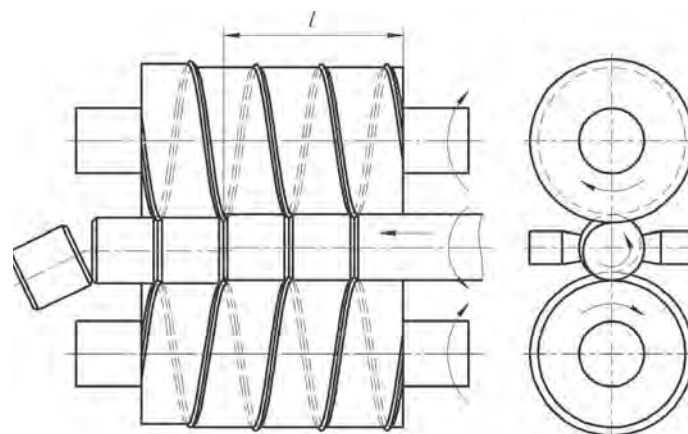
Схема разделения прутка на заготовки винтовой прокаткой
